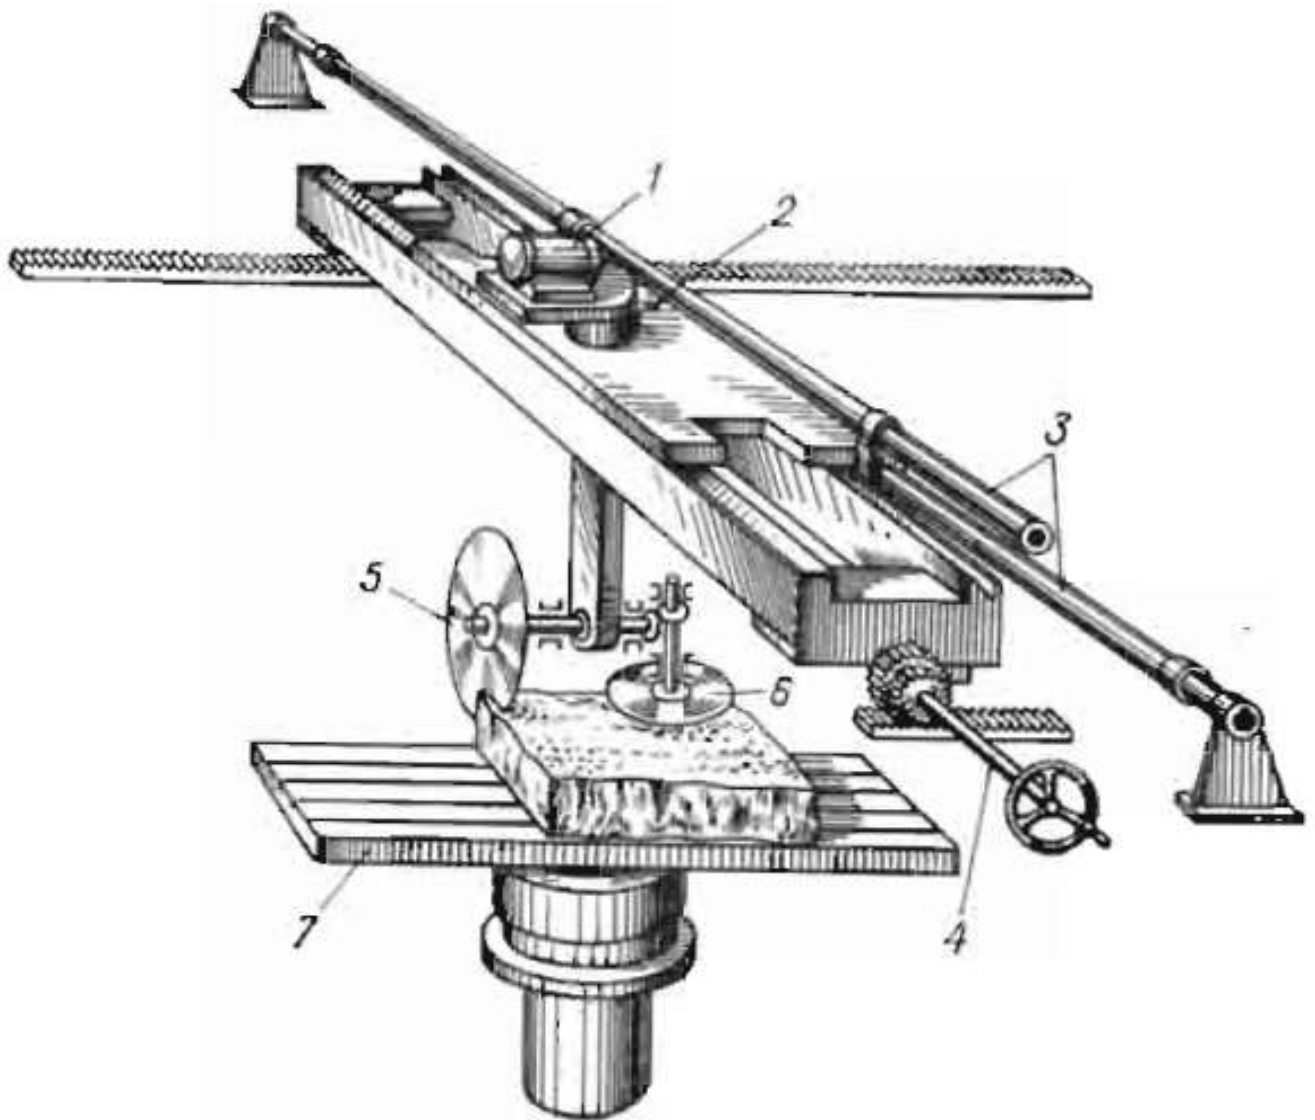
Обкантовочно-фрезерний мостовий верстат СМР-015 [3]: кінематична схема.
